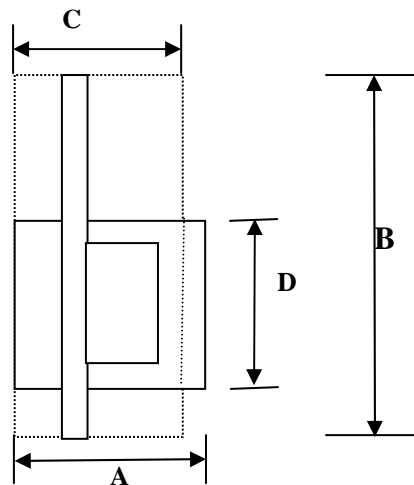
Dimensiões CB_01_DIN. A parte delimitada representa a tampa de plexiglas
